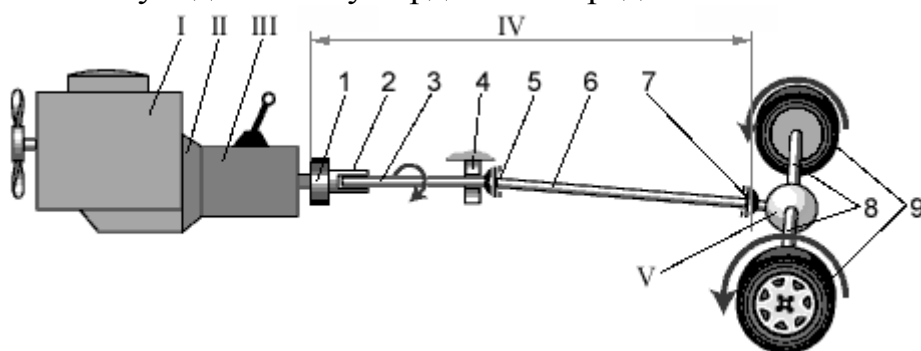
Схема трансмиссии заднеприводного автомобиля I - Двигатель; II - Сцепление; III - Коробка передач; IV - Карданная передача: 1 - эластичная муфта; 2 - шлицевое соединение; 3 - передний карданный вал; 4 - подвесной подшипник; 5 - передний карданный шарнир; 6 - задний карданный вал; 7 - задний карданный шарнир; V - Задний мост с главной передачей и дифференциалом: 8 - полуоси; 9 - ведущие (задние) колеса
